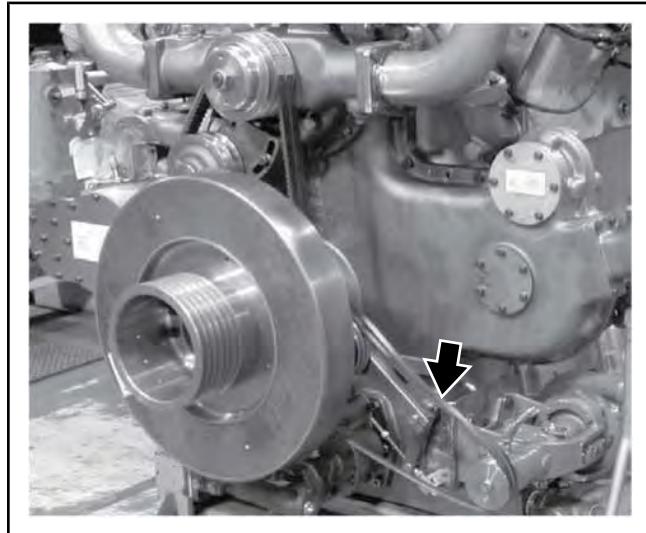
Регулировка узла промежуточного рычага
